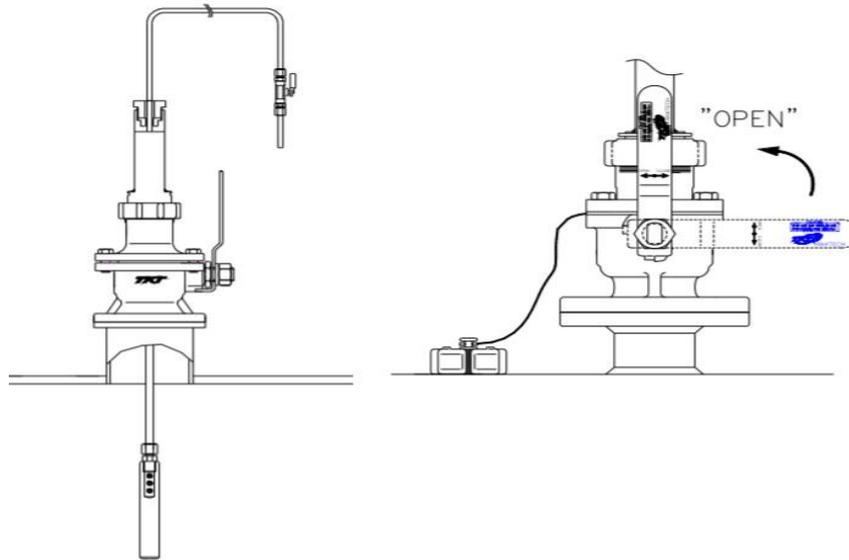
Vapor Lock. Fuente: TANKTECH, Instruction manual for inert gas sampling hose and adaptor
